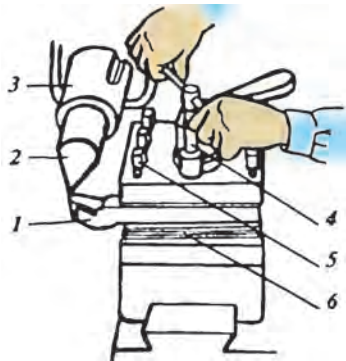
Установление токарного резца на держатель: 1 – резец; 2 – задний центр; 3 – пинол задней бабки; 4 – ключи; 5 – винты для закрепления резца; 6 – поддоны резца.
